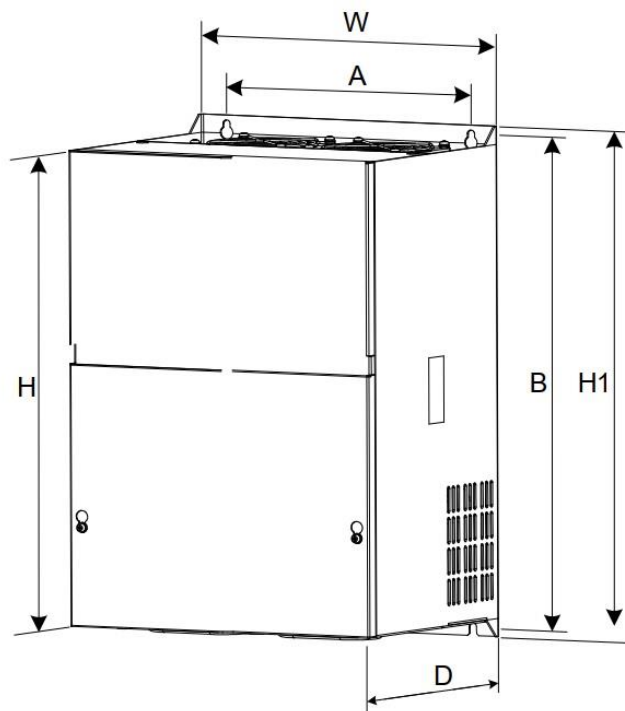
Схема размеров для монтажа INVERTER (18.5–45 кВт, корпус из листового металла)
